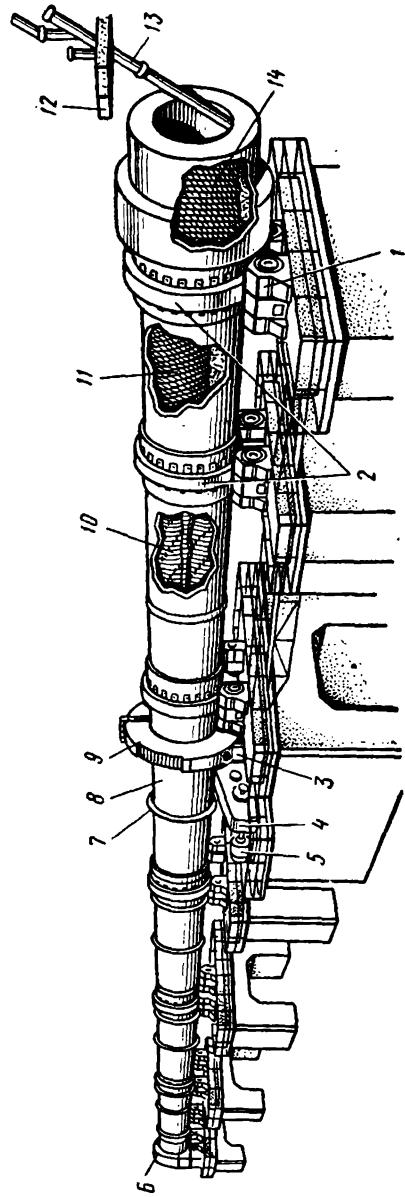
Длинная вращающаяся печь с теплообменными устройствами внутри корпуса:
